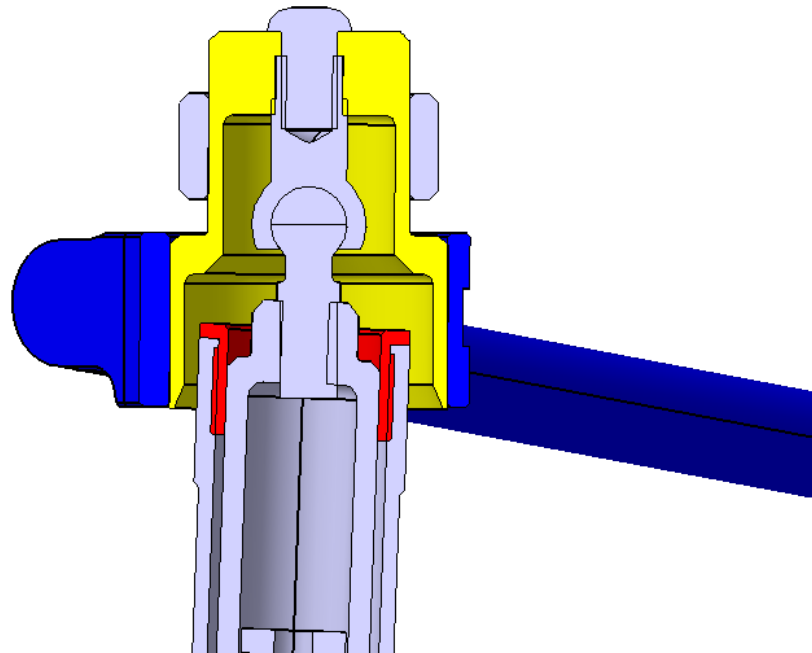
Corte de la pieza MT2-DI-00-03 en su montaje final con la suspensión totalmente comprimida.
